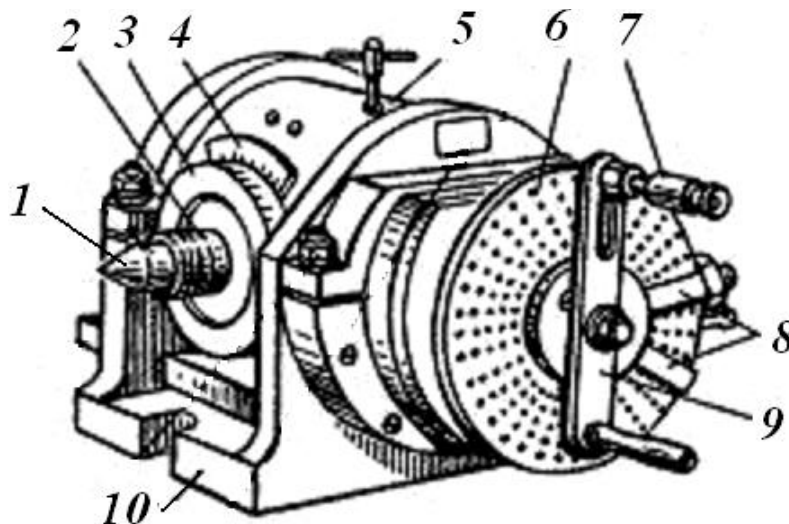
Загальний вигляд УДГ: 1 – центр, 2 – шпиндель, 3 – лімб, 4 – ноніус, 5 – корпус, 6 – ділильний диск, 7 – фіксатор, 8 – розсувний сектор, 9 – рукоятка, 10 - основа
